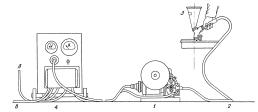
Схема плангового полуавтомата IIIII-5: 1- подающий механизм; 2- специальный шланговый провод; 3- держатель; 4- аппаратный
